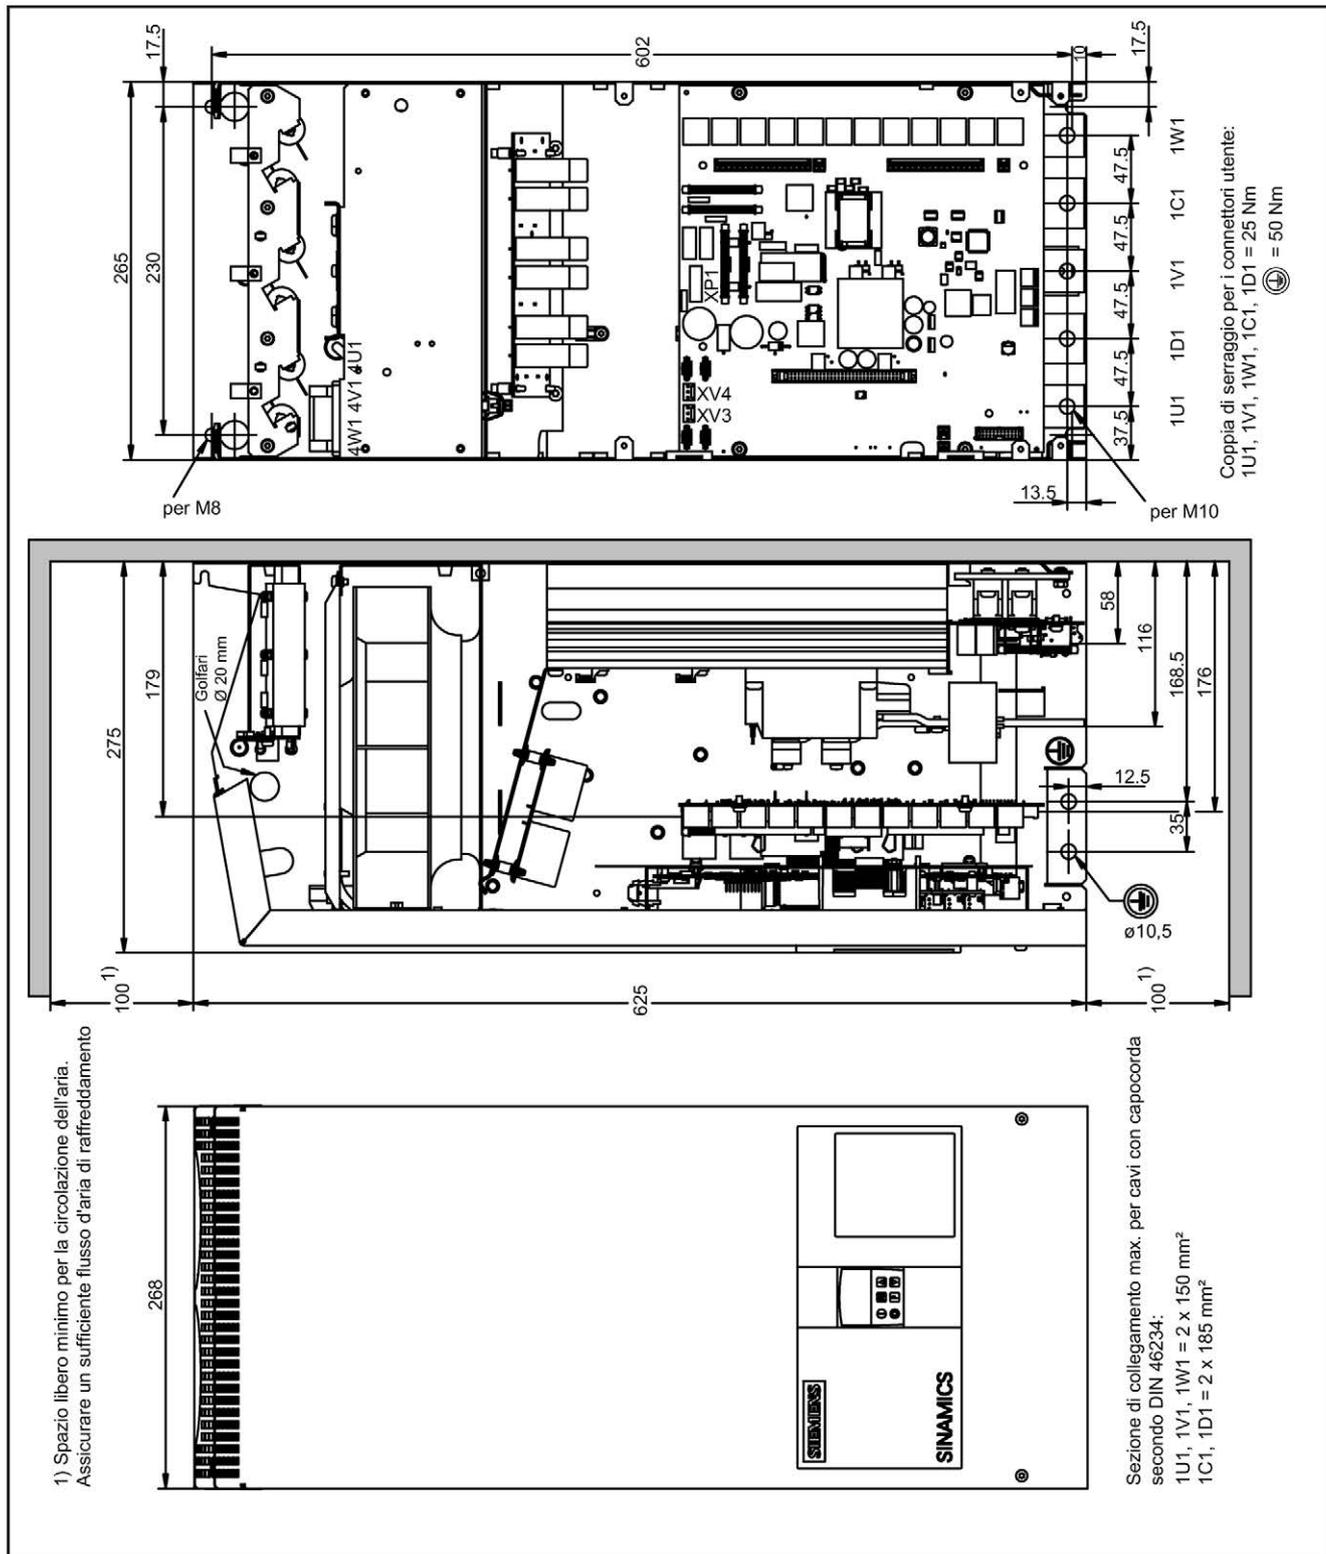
Disegno quotato 400 A ... 600 A, 2Q
